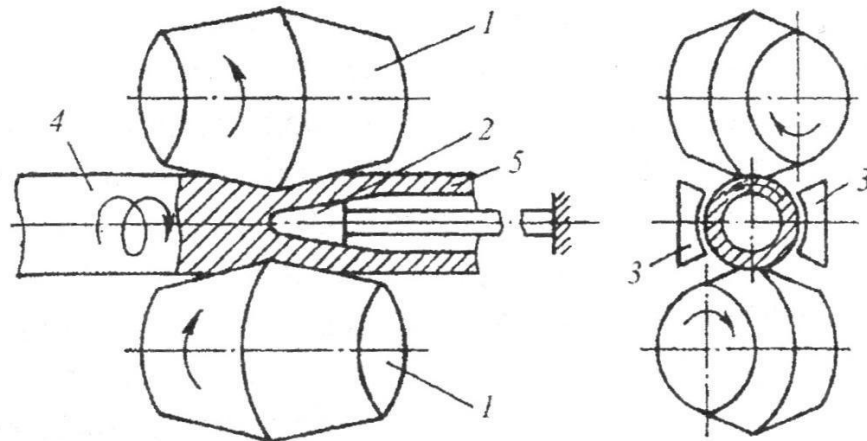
Схема поперечного-гвинтового прокатування при прошиванні отвору в суцільному матеріалі: 1 – прокатні валки; 2 – оправка; 3 – лінійки; 4 – оброблюваний матеріал; 5 – отриманий розкат.
